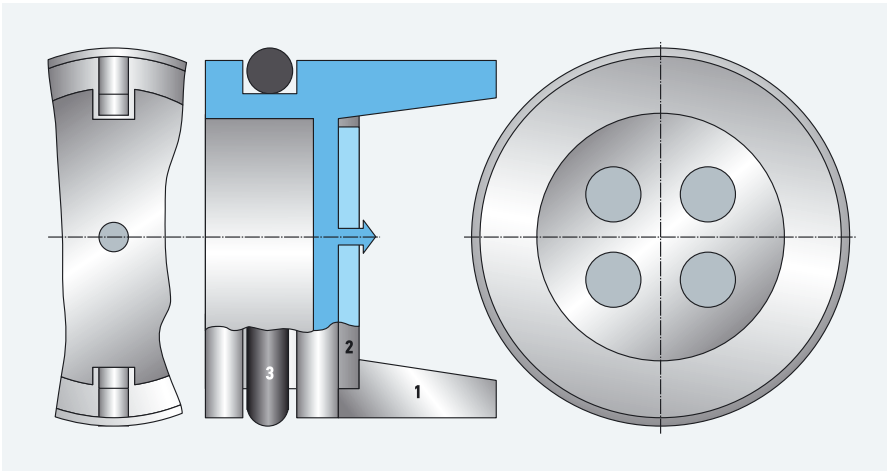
Конструктивная схема обратного клапана с защитой от воздуха (1 — корпус; 2 — эластичное уплотнение; 3 — уплотнительное кольцо)
